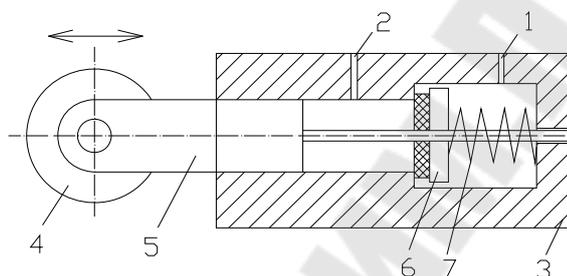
Двухпозиционный путевого пневматический концевой выключатель
